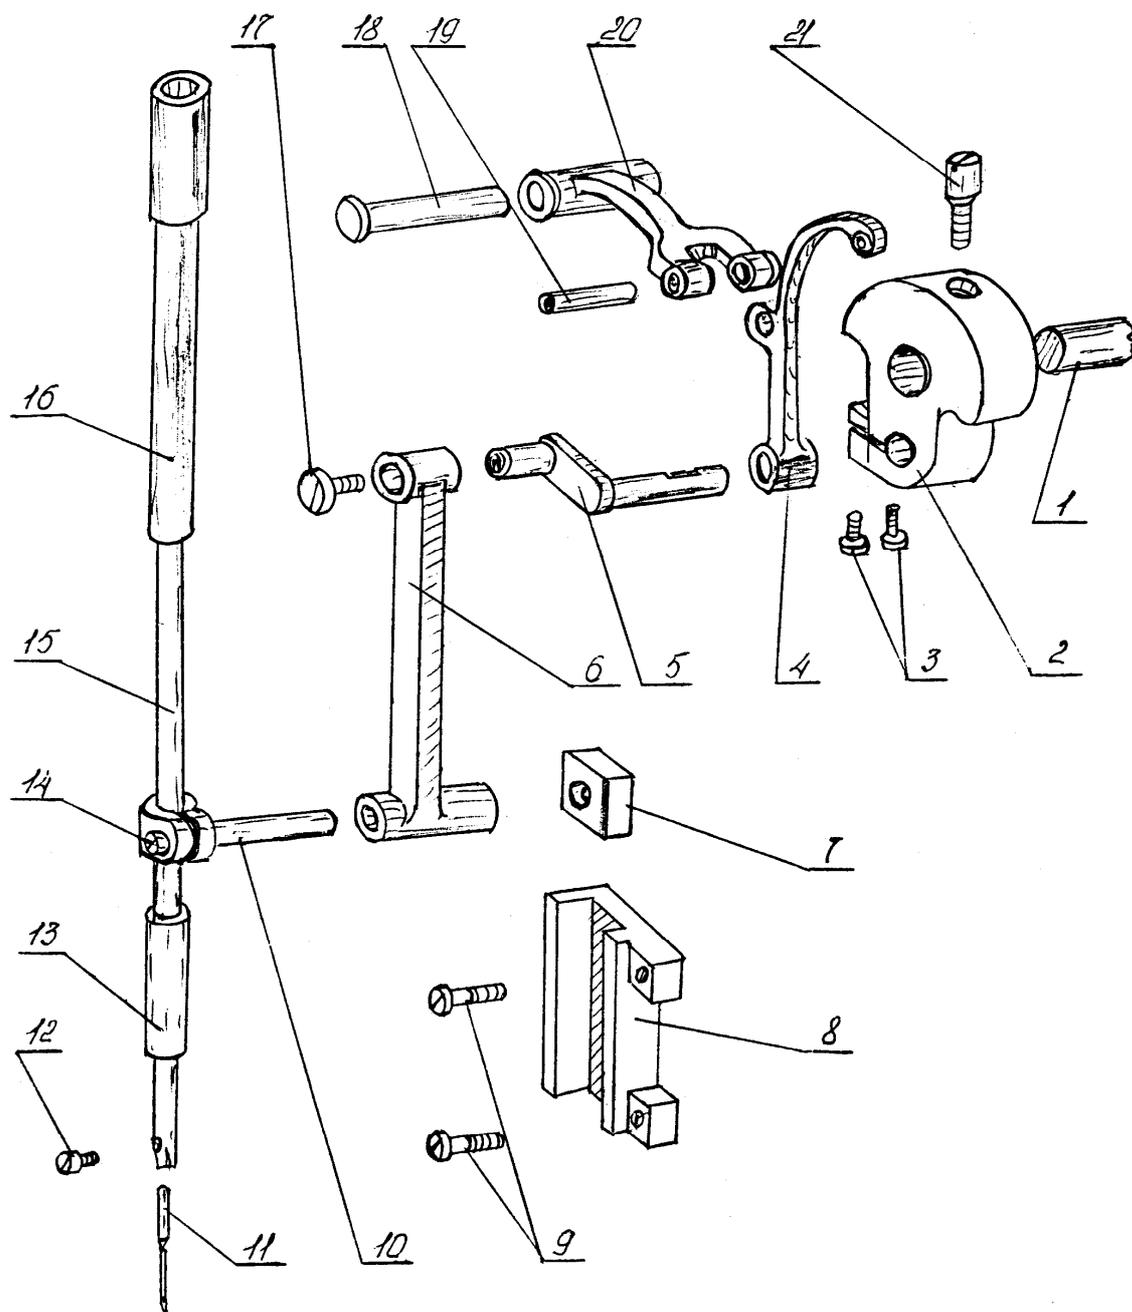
Механизм иглы и нитепритягивателя
